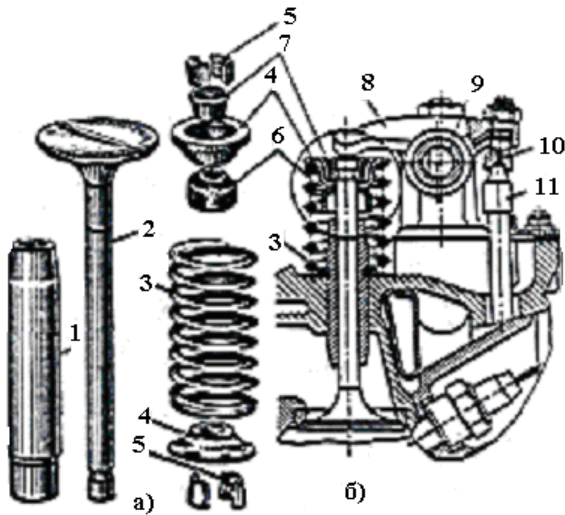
Деталі групи клапана двигуна за різноманітного розташування клапанів
